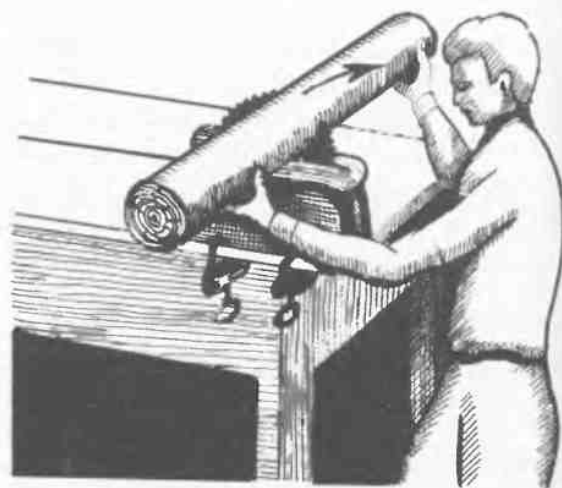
Недозволенный прием пиления — опасный момент отброса заготовки в сторону пильщика
